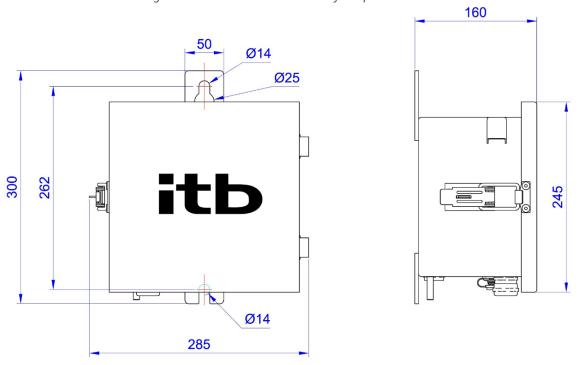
Dimensión exterior de la caja de paso auxiliar.
